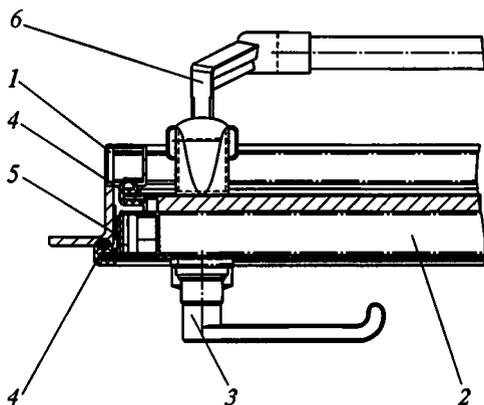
Дверной противопожарный блок кабины машиниста:
